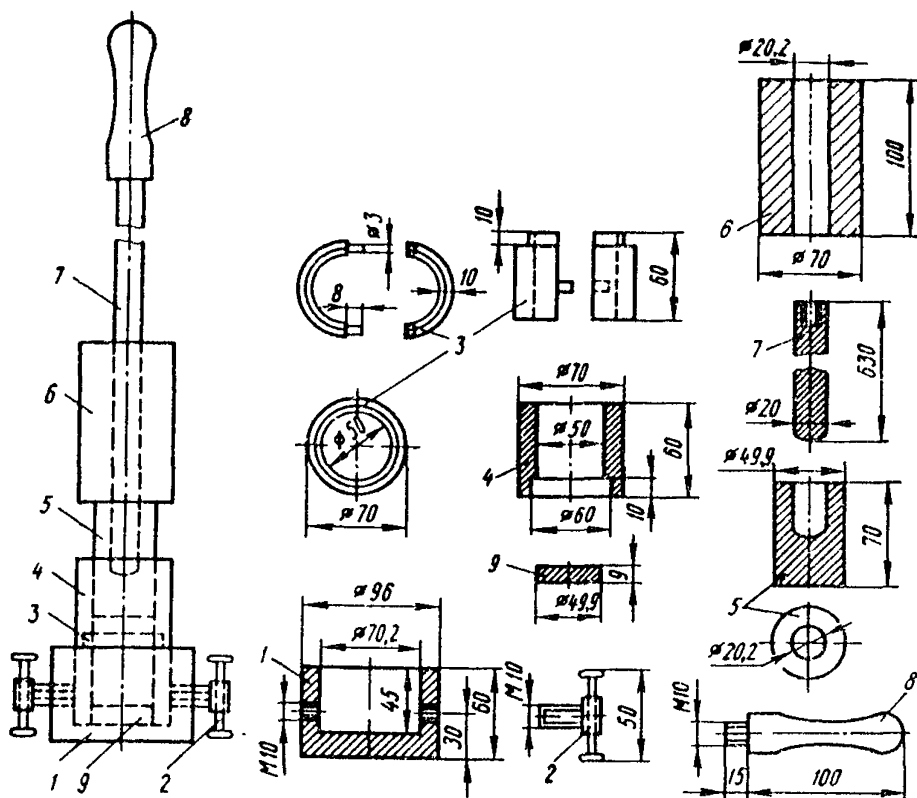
Схема малого прибора стандартного уплотнения: 1 - подставка; 2 - закрепляющие винты; 3 - разъемный цилиндр; 4 - направляющий насадный цилиндр; 5 - плунжер, передающий ударную нагрузку; 6 - гиря массой 2,5 кг; 7 - направляющий стержень; 8 - рулетка; 9 - пластина для подставки в разъемный цилиндр
